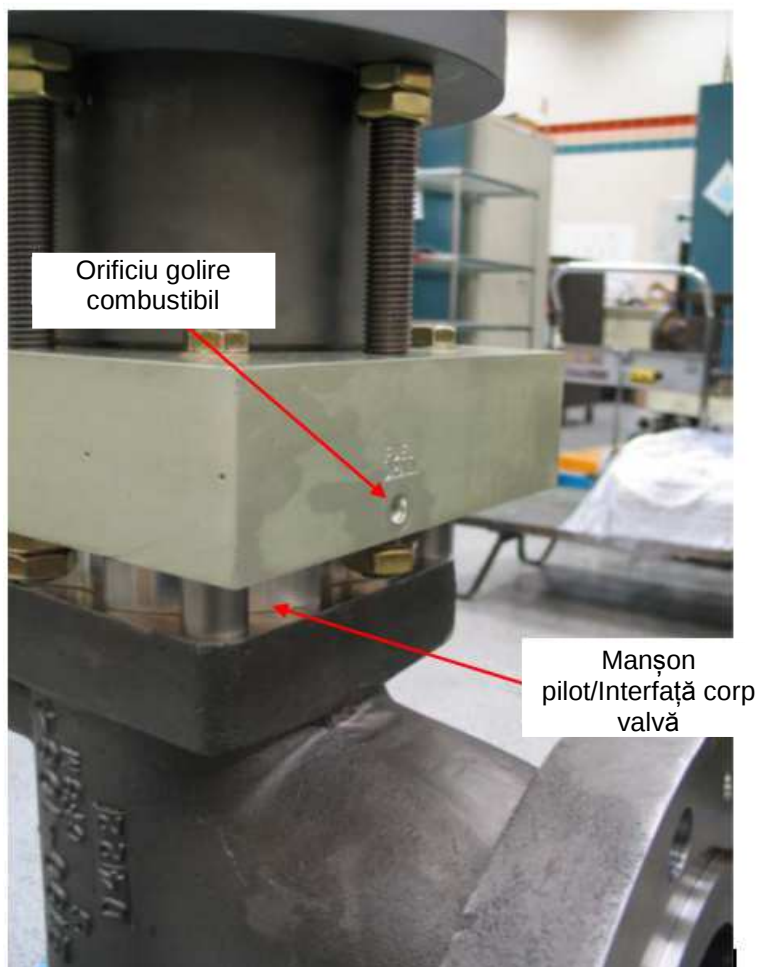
Zone de inspecție pentru valve de 3, 4 și 6 țoli
